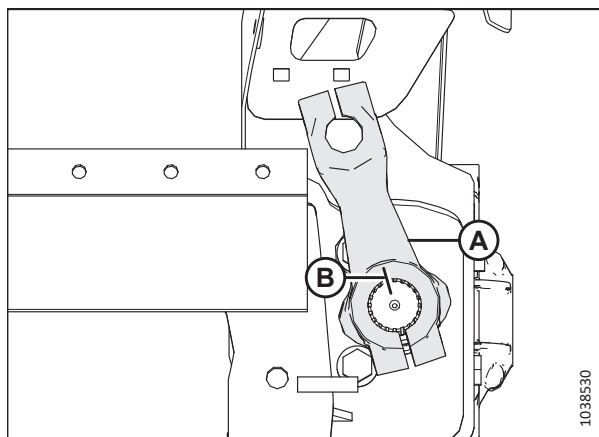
Braço de acionamento da navalha – Vista inferior
